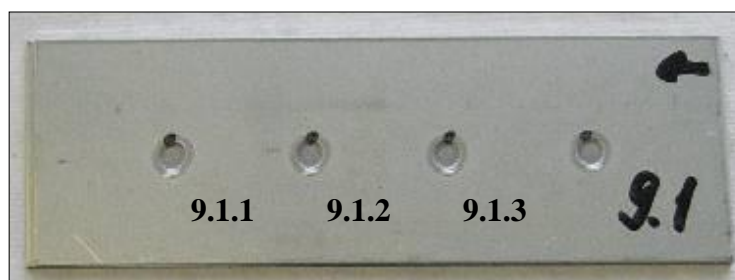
Внешний вид точечной контактной сварки образца № 9.1
